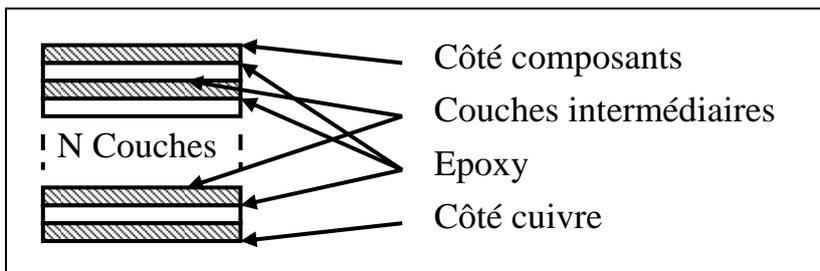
vue en coupe d'une plaque multicouches.
